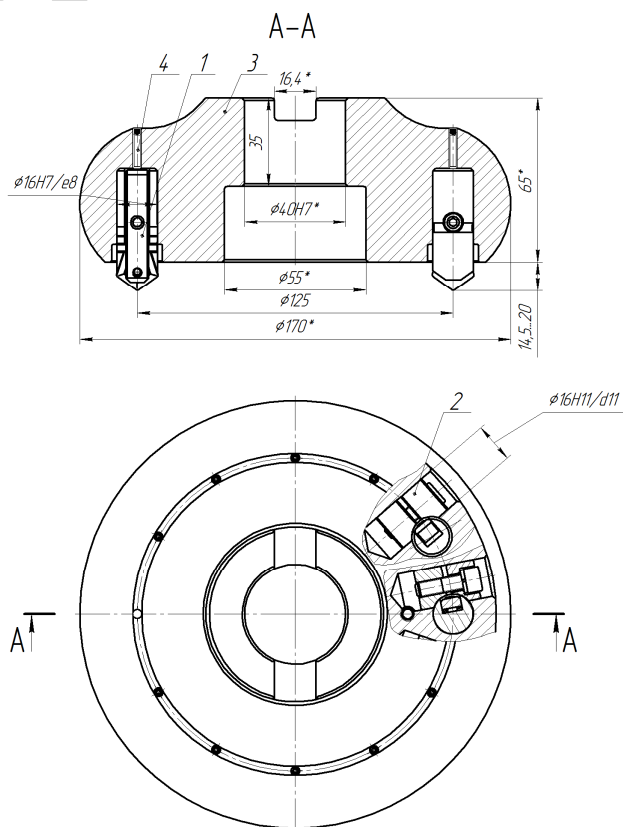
Вариант конструкции торцовой блочно-модульной фрезы с обтекаемой формой корпуса: 1 – блок резцовый; 2 – модуль зажимной; 3 – модуль корпусной; 4 – винт регулировочный
